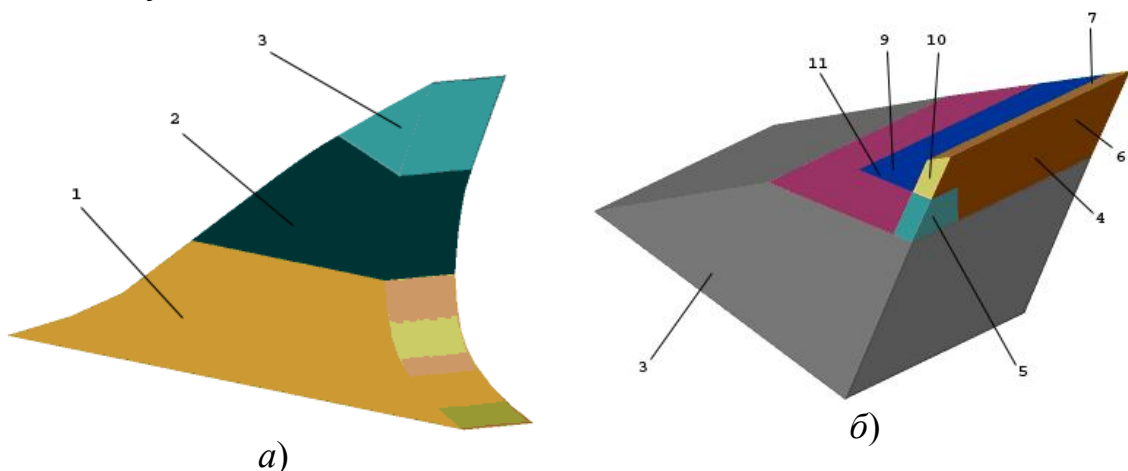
Твердотільна модель розведеного зубця стрічкової пилки другого типу: а) зубець; б) верхня частина зубця
